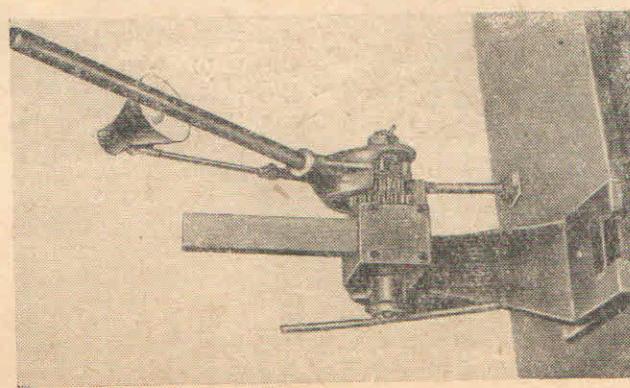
Приспособление для заполнения пресс-форм сырой резиной:
